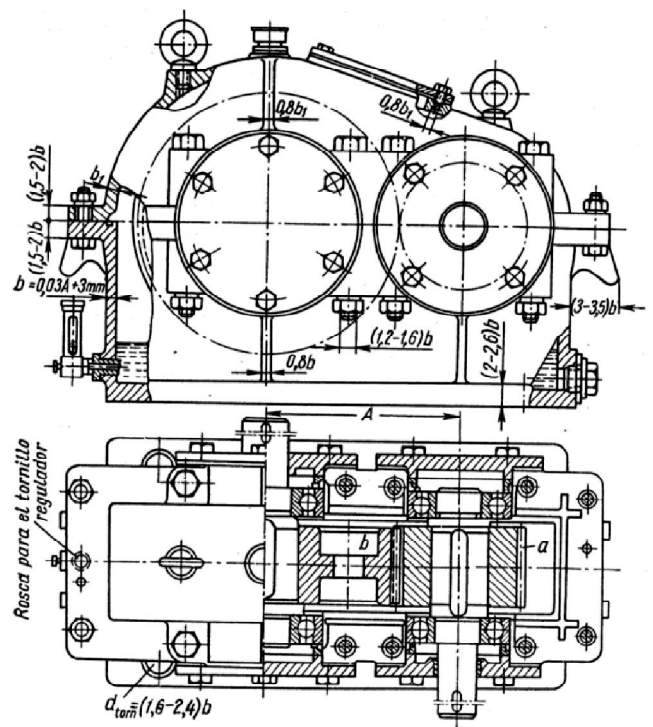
reductor de engranajes cilíndricos de 1 etapa (Ref.1)
